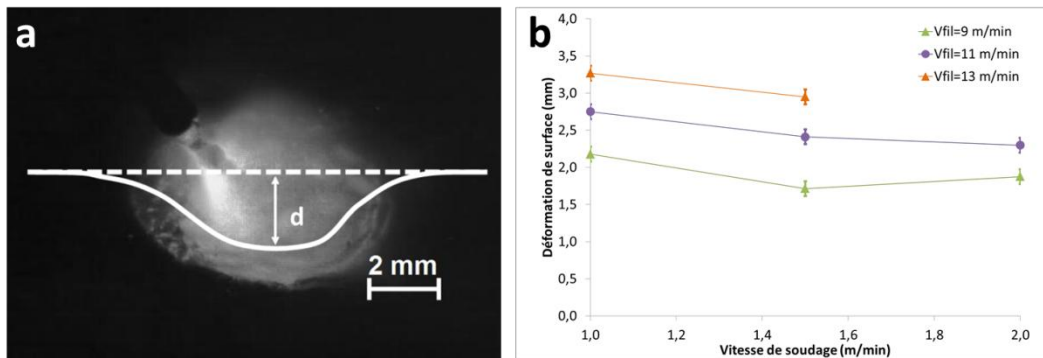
Mesures de la déformation de surface (a) et résultats obtenus en fonction de la vitesse de soudage (b) en soudage hybride laser-MAG
